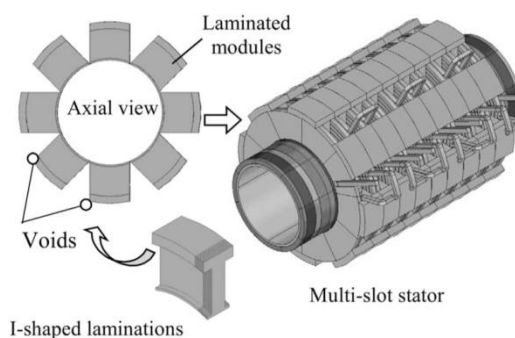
Магнитопровод статора, изготовленный из модулей, шихтованных I-образными листовыми заготовками.
